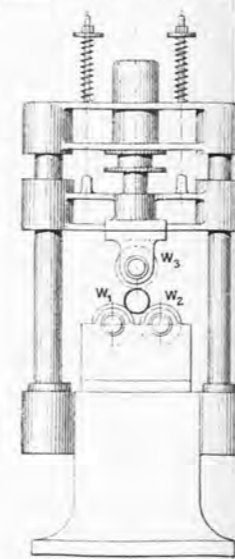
Walzwerk zur Herstellung geschweißter Hohlkörper.
